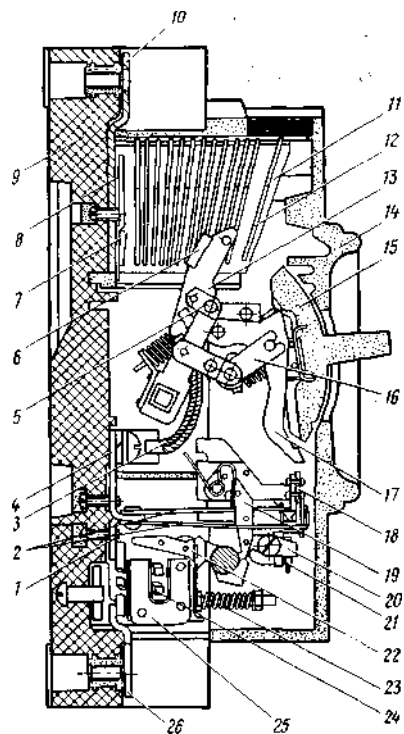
Установочный автоматический выключатель серии АЗ300
